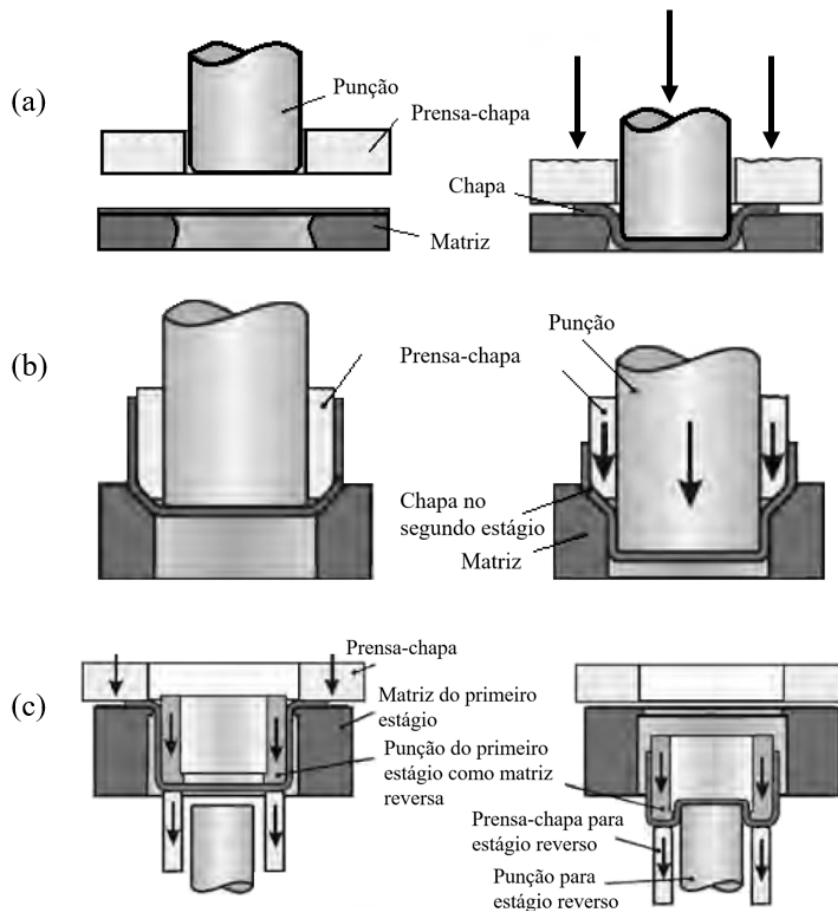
Operações de estampagem: (a) Estampagem com prensa-chapa; (b) estampagem em múltiplos estágios e (c) estampagem reversa. Fonte: Adaptado de ALTAN e TEKKAYA, 2012
